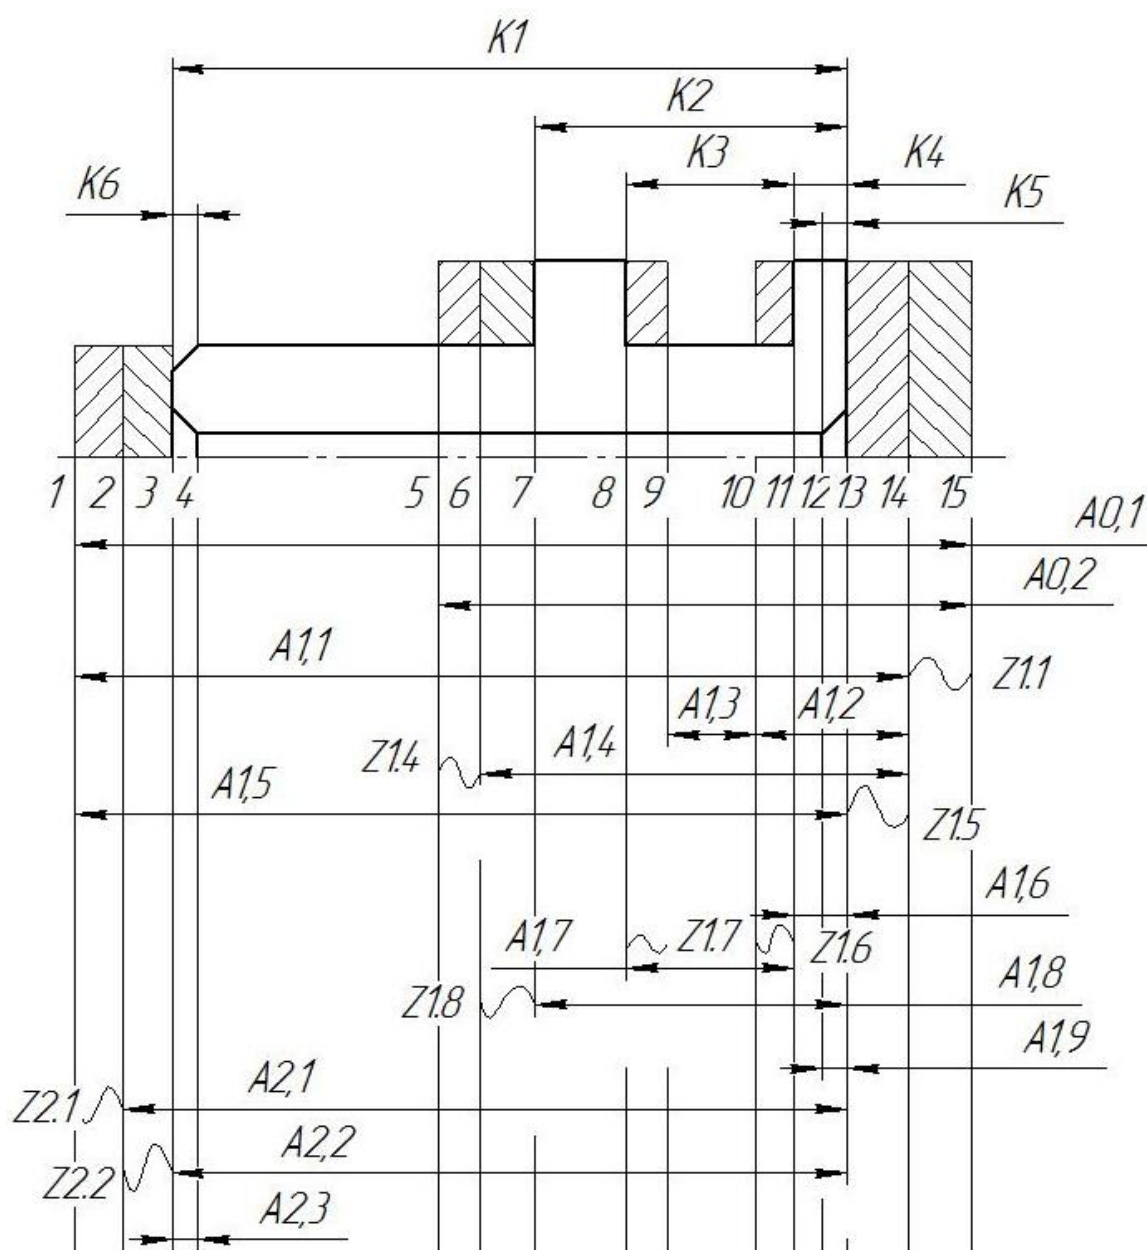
Размерная схема технологического процесса изготовления детали «Втулка включения»(продольное направление)
